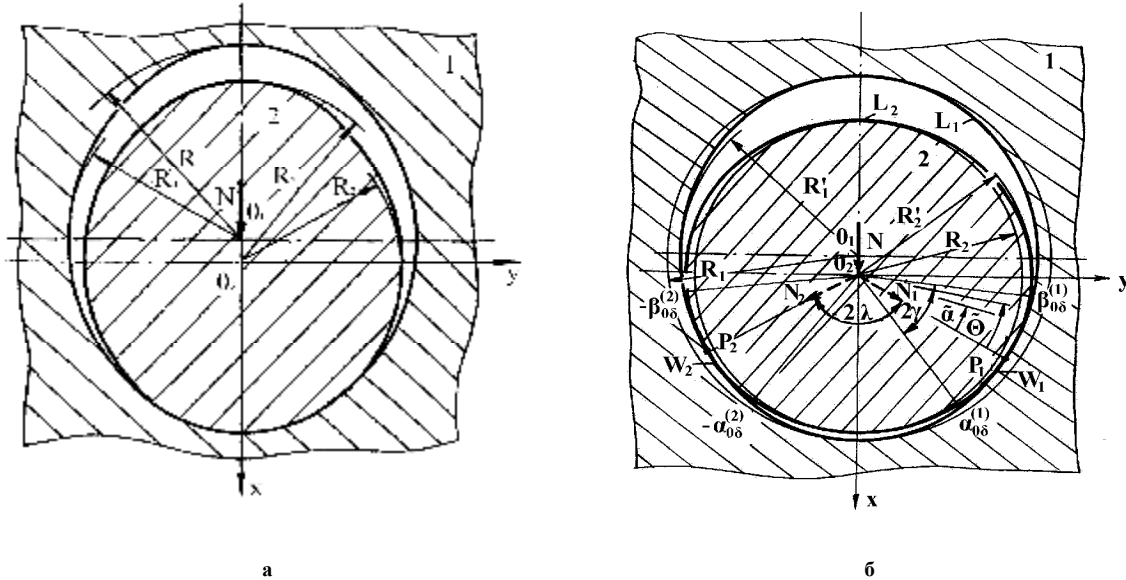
Розрахункова схема підшипника з овальністю деталей:
